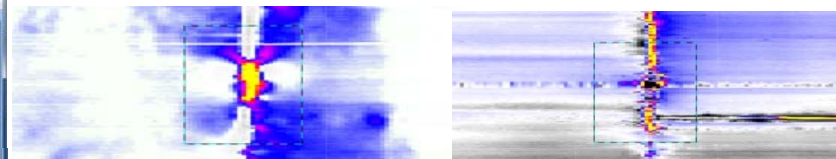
Смещение кромок на кольцевом сварном шве
